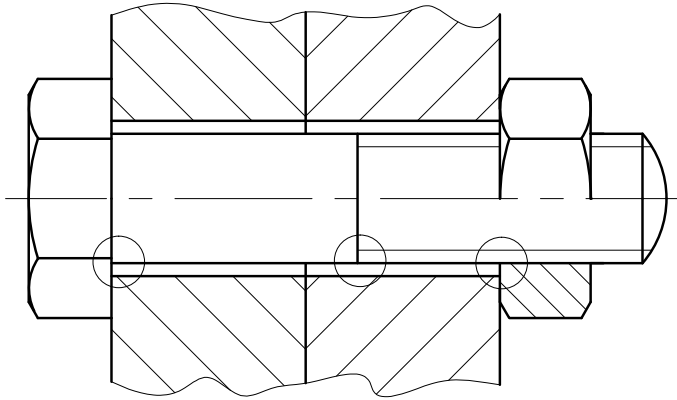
Kritische Stellen einer Sechskantschraube hinsichtlich Belastung
